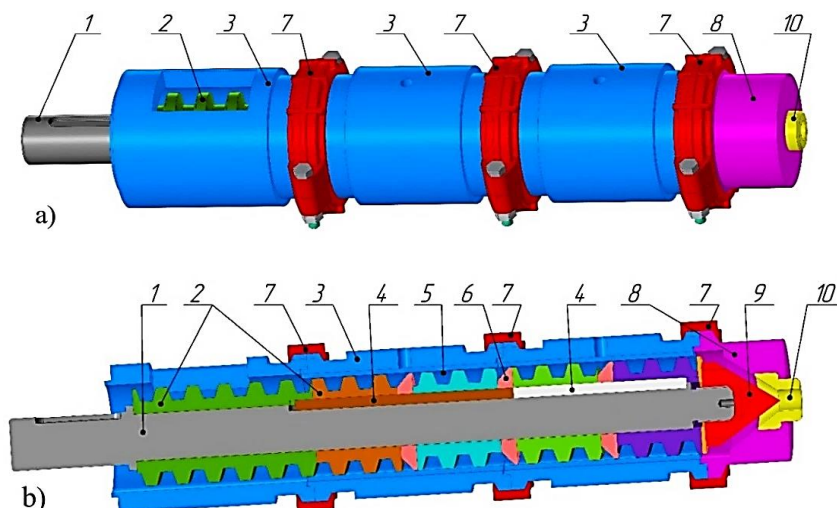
Устройство шнековой группы экструдера: 1 – вал шнека; 2 – питающие секции шнека; 3 – корпус; 4 – шпонка; 5 – пазы противотока корпуса; 6 – компрессионный затвор; 7 – хомуты соединительные; 8 – съемная регулировочная матричная головка; 9 – конусная головка шнекового вала; 10 – фильера
